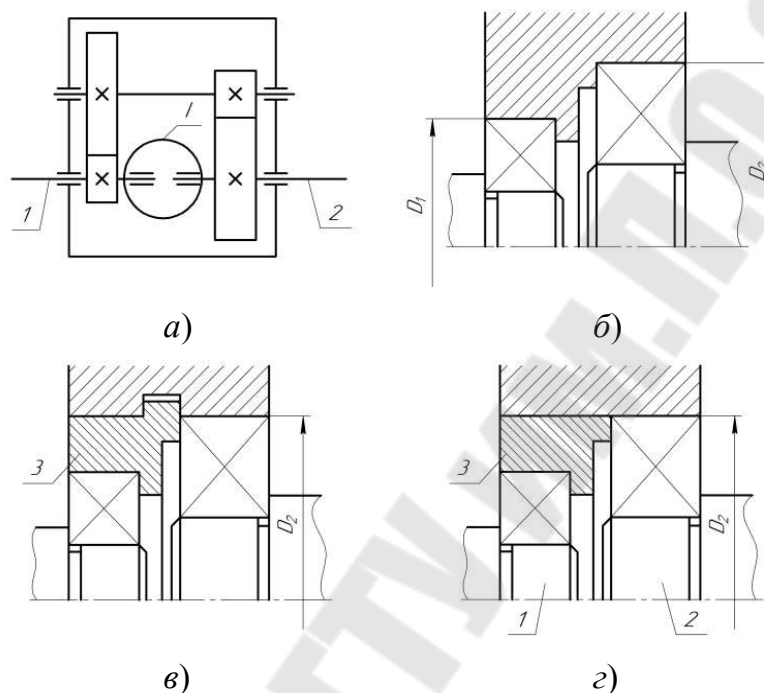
Схема и установка подшипников внутренней опоры соосного редуктора:
